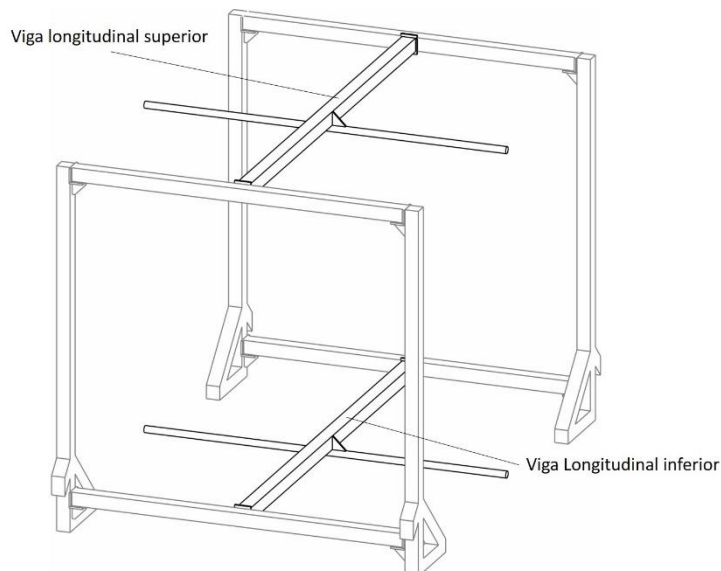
Columnas de soporte de la estructura del banco KLT.
